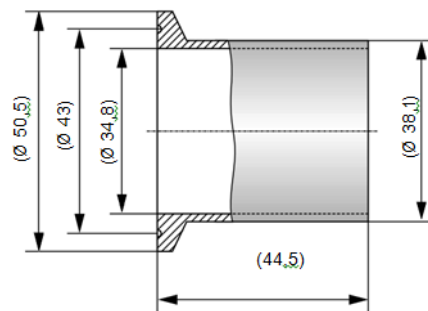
Tri-Clamp Anschweißstutzen
